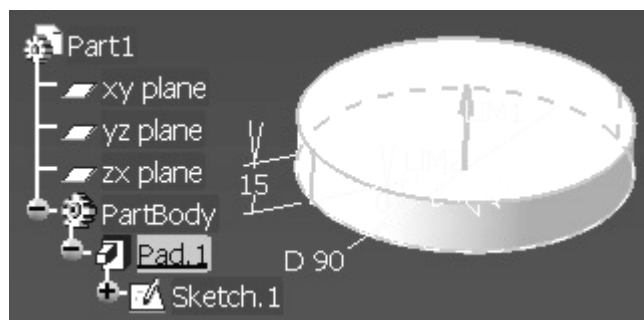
Obținerea primului cilindru (corpul flanșei)
